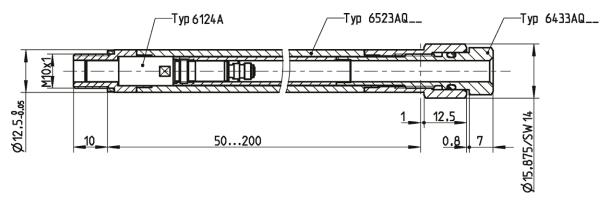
Montagehülse Typ 6523AQ mit M10x1 Druckstück Typ 6433AQ
